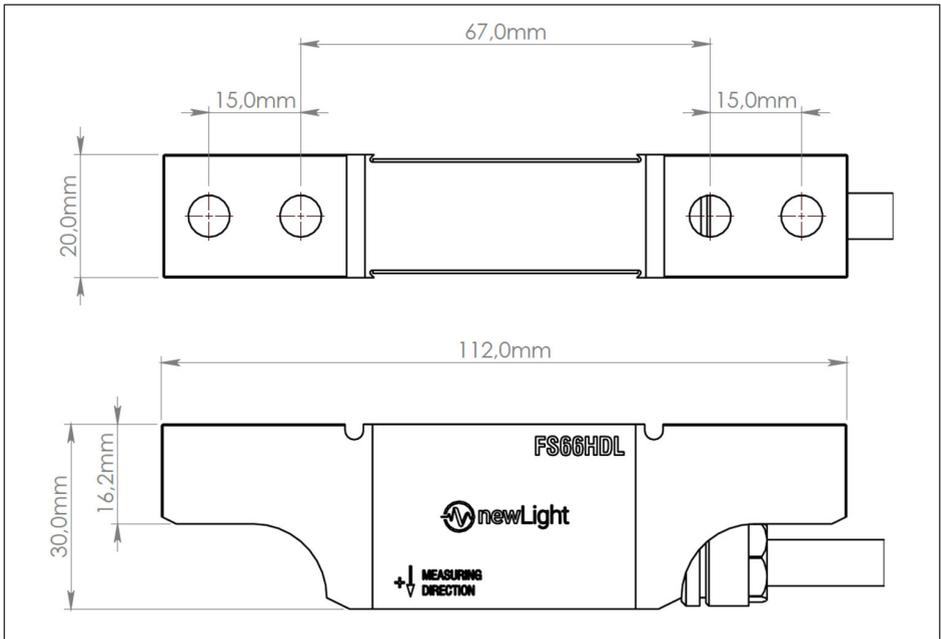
Dessin technique du capteur de force Heavy Duty FS66HDL (dimensions en mm)
